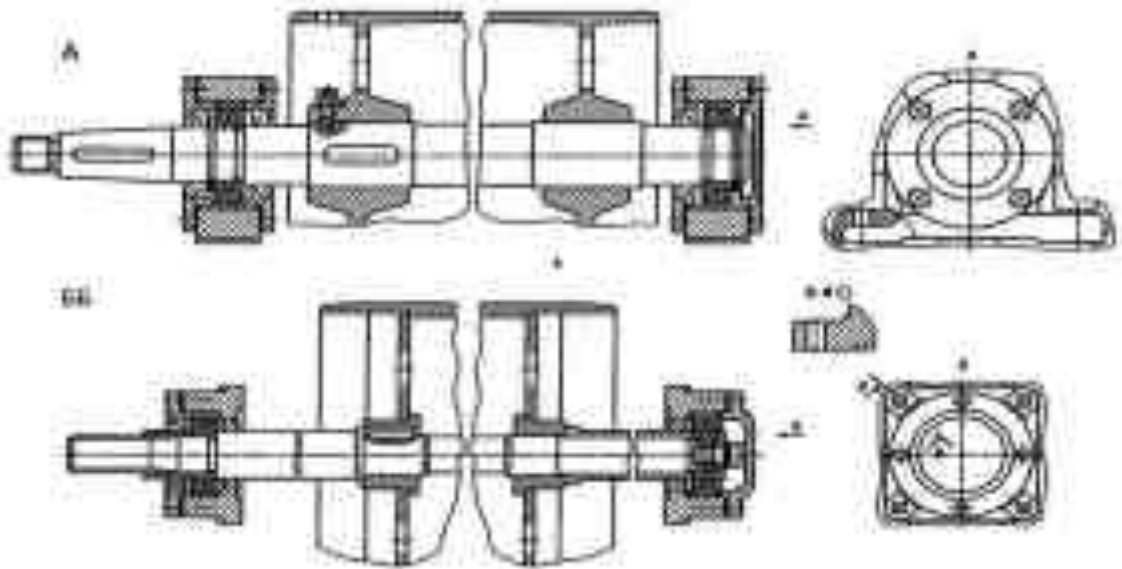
Барабани приводні на валу: А – литий; Б - зварний
